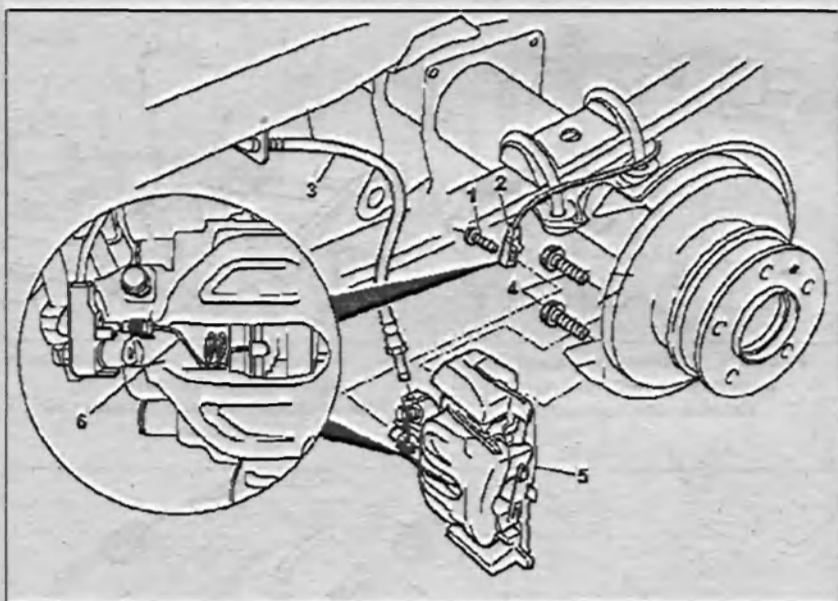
Тормозной суппорт заднего тормозного механизма:
